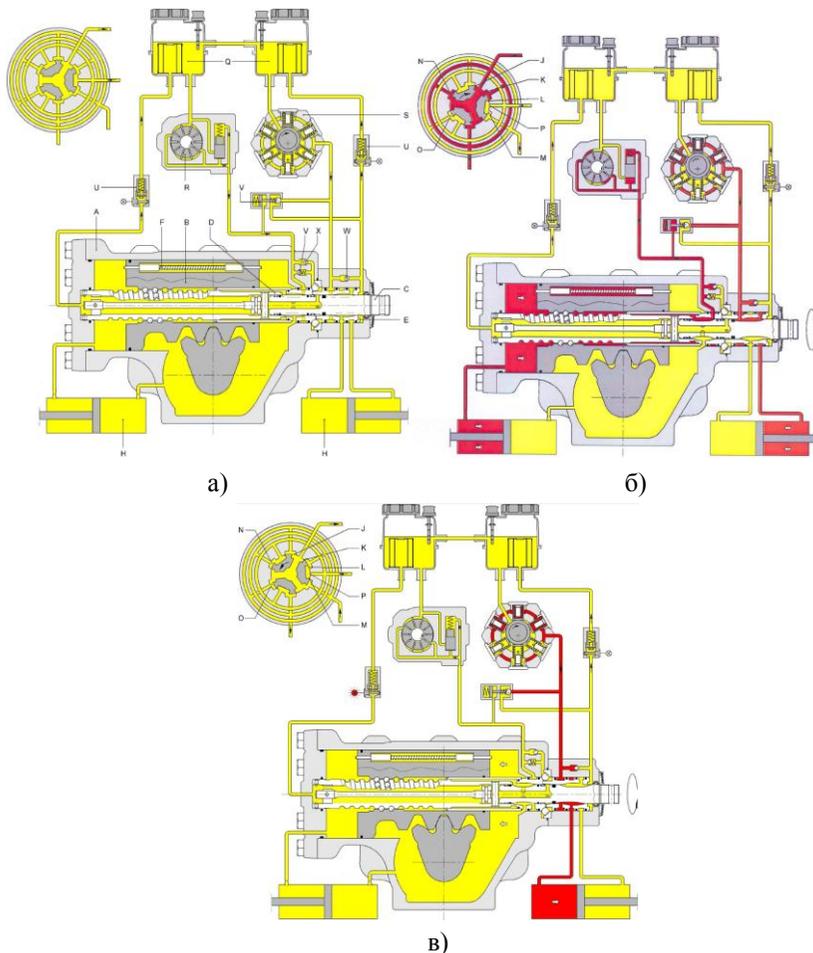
Двухконтурный гидравлический усилитель руля с двумя насосами, двумя распределителями и двумя вспомогательными цилиндрами (двухпоршневым вспомогательным цилиндром):
